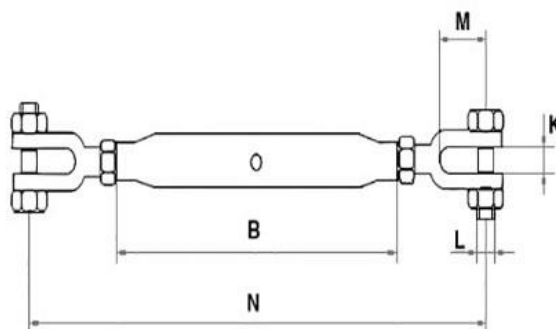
Чертеж талрепа вилка-вилка (закрытого типа).
